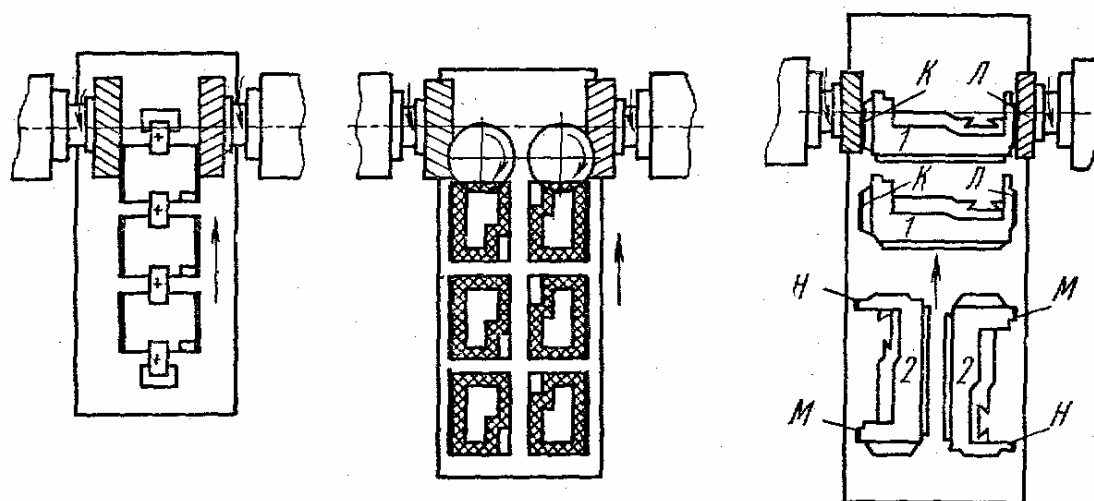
Схема групповой обработки на продольно-фрезерном станке
